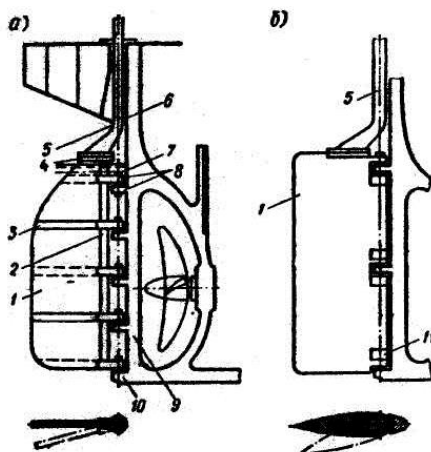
Небалансирные рули: 1 – перо руля; 2 – рудерпис; 3 – ребро; 4 – фланцевое соединение; 5 – баллер; 6 – гельмпортная труба; 7 – штыри; 8 – петли; 9 – рудерпост; 10 – пятка ахтерштевня; 11 – защитные кожухи штырей
